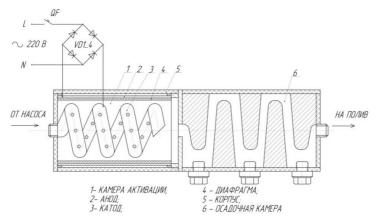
Схема проточного электроактиватора: 1 – камера активации; 2 – анод; 3 – катод; 4 – диафрагма; 5 – корпус; 6 – осадочная камера
